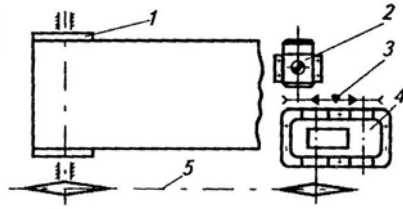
Схема стрічкового конвеєра: 1 – приводний шків; 2 – привод; 3 – стійки; 4 – натяжний шків; 5 – металеві напрямні; 6 – верхня гілка стрічки
